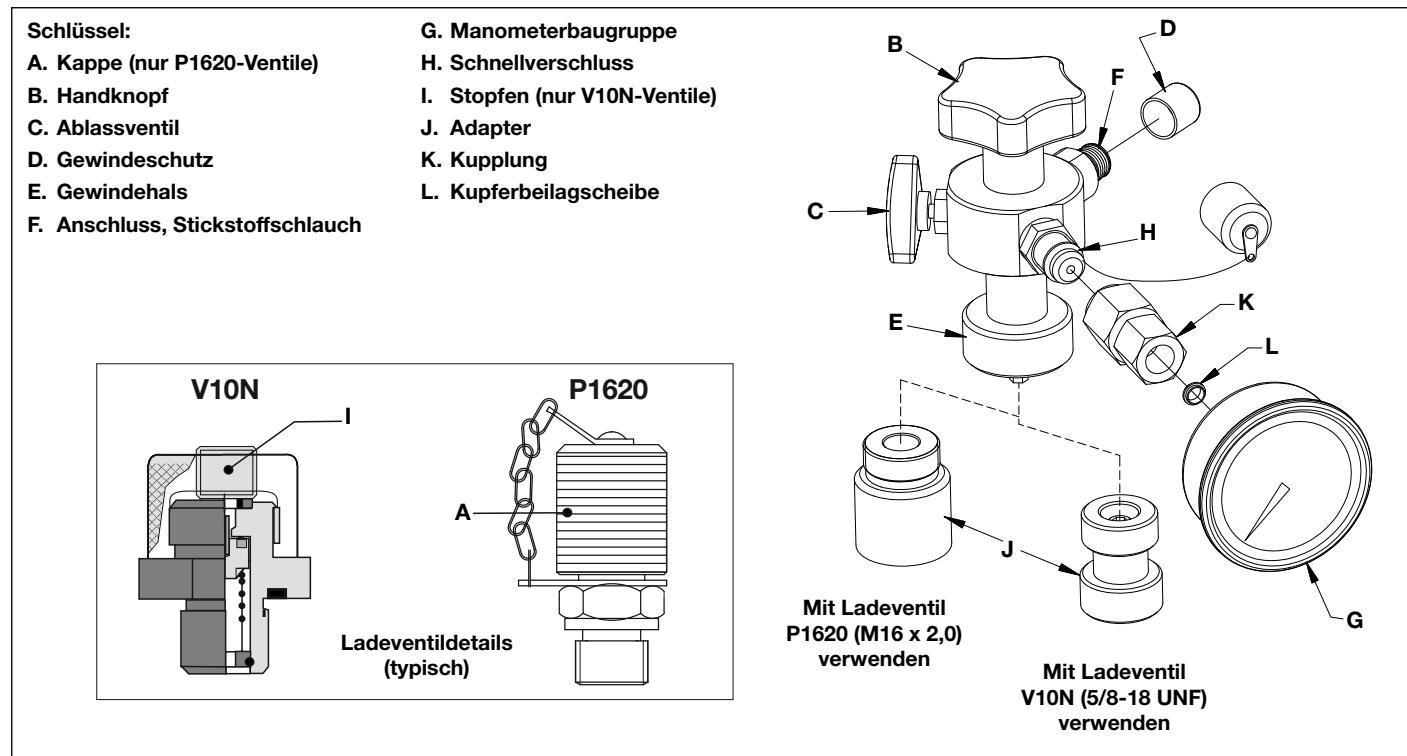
, WAT-2A Ladewerkzeug und Adapter
